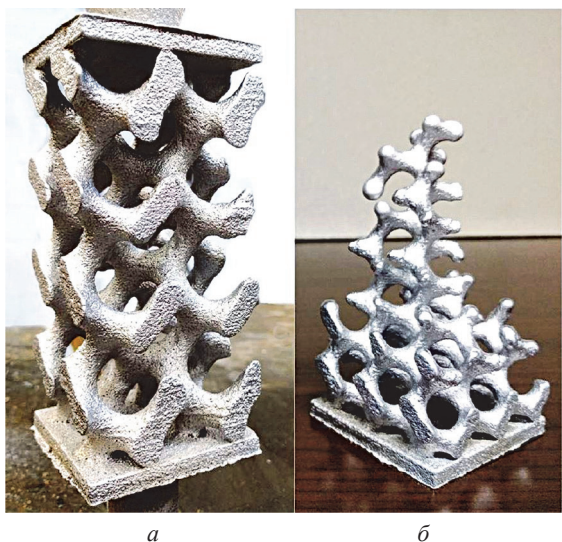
Отливки ячеистой конструкции с разной степенью заполнения металлом песчаной формы аддитивного производства: *а* – отливка решетки, так называемой гироидной конструкции; *б* – «недолив» такой же отливки
